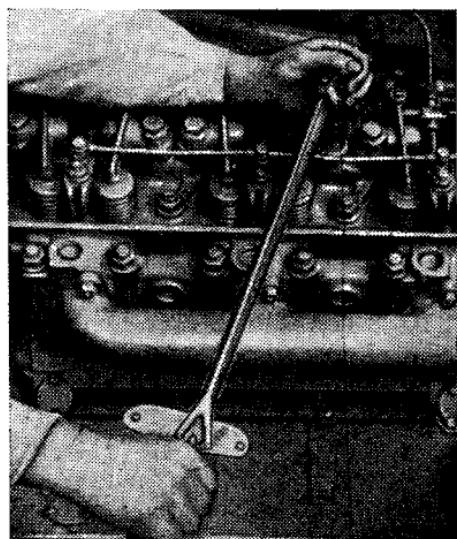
Проверка момента затяжки болтов крепления осей коромысел
